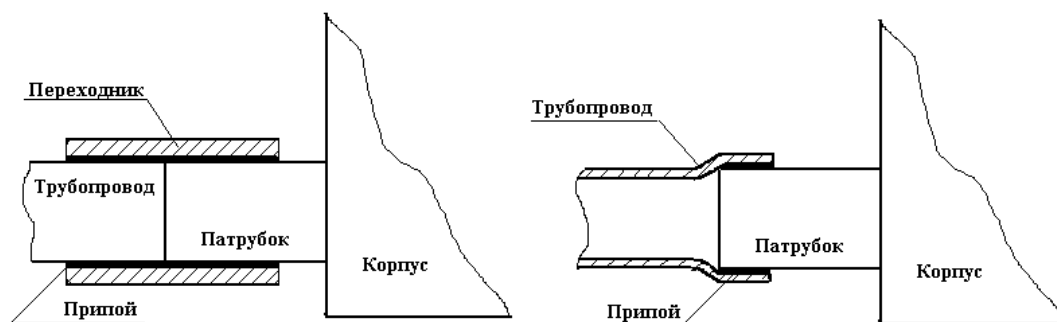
Способы соединения патрубка агрегата компрессорного с трубопроводом
